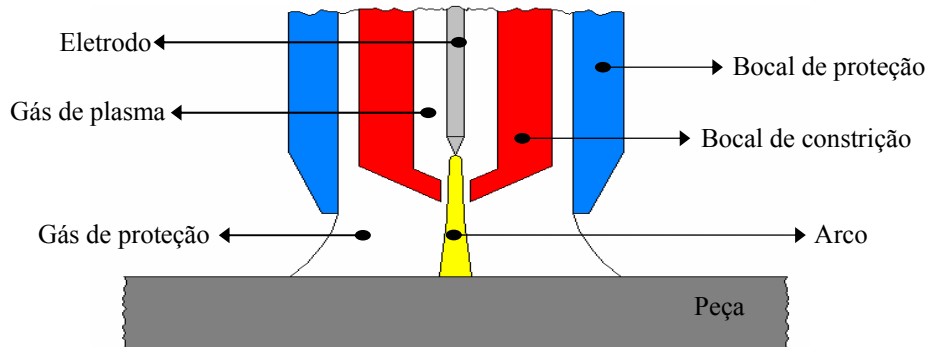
Representação esquemática do processo de soldagem Plasma “melt-in”
